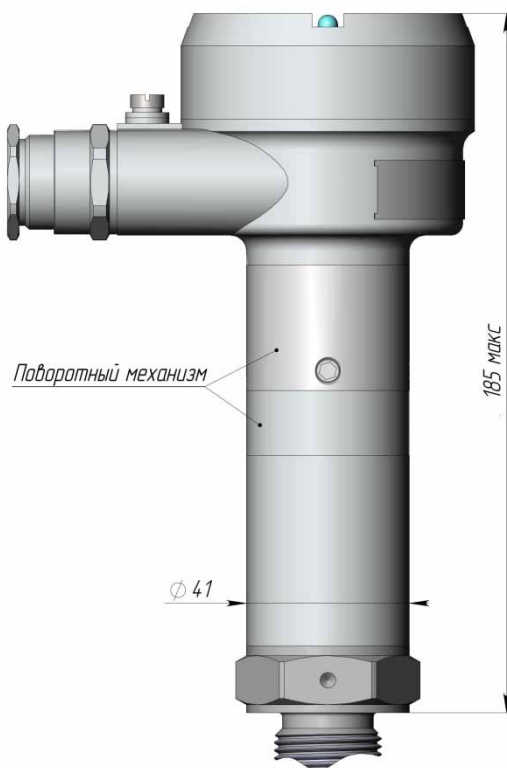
Габаритные размеры перехода на 250°C с поворотным механизмом (или газонепроницаемый)
